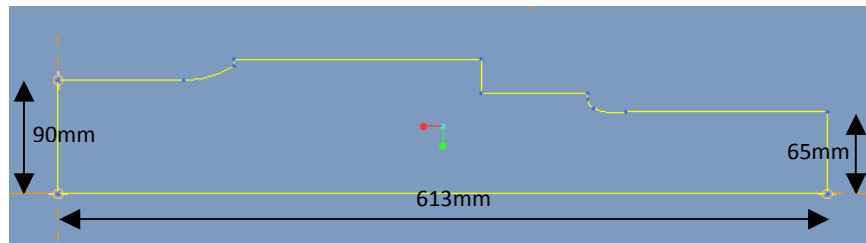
Sección de la viga del problema “Viga empotrada 2”
